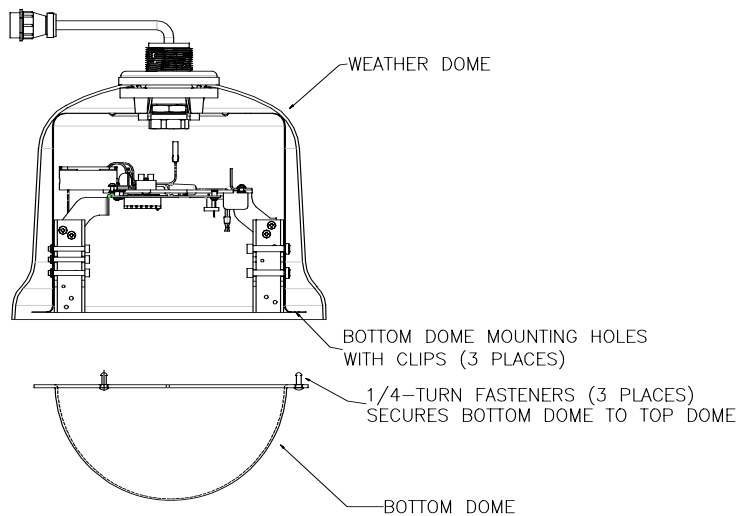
INSTALLAZIONE, CUPOLA INFERIORE SULLA DOME CON TERMOVENTILAZIONE
